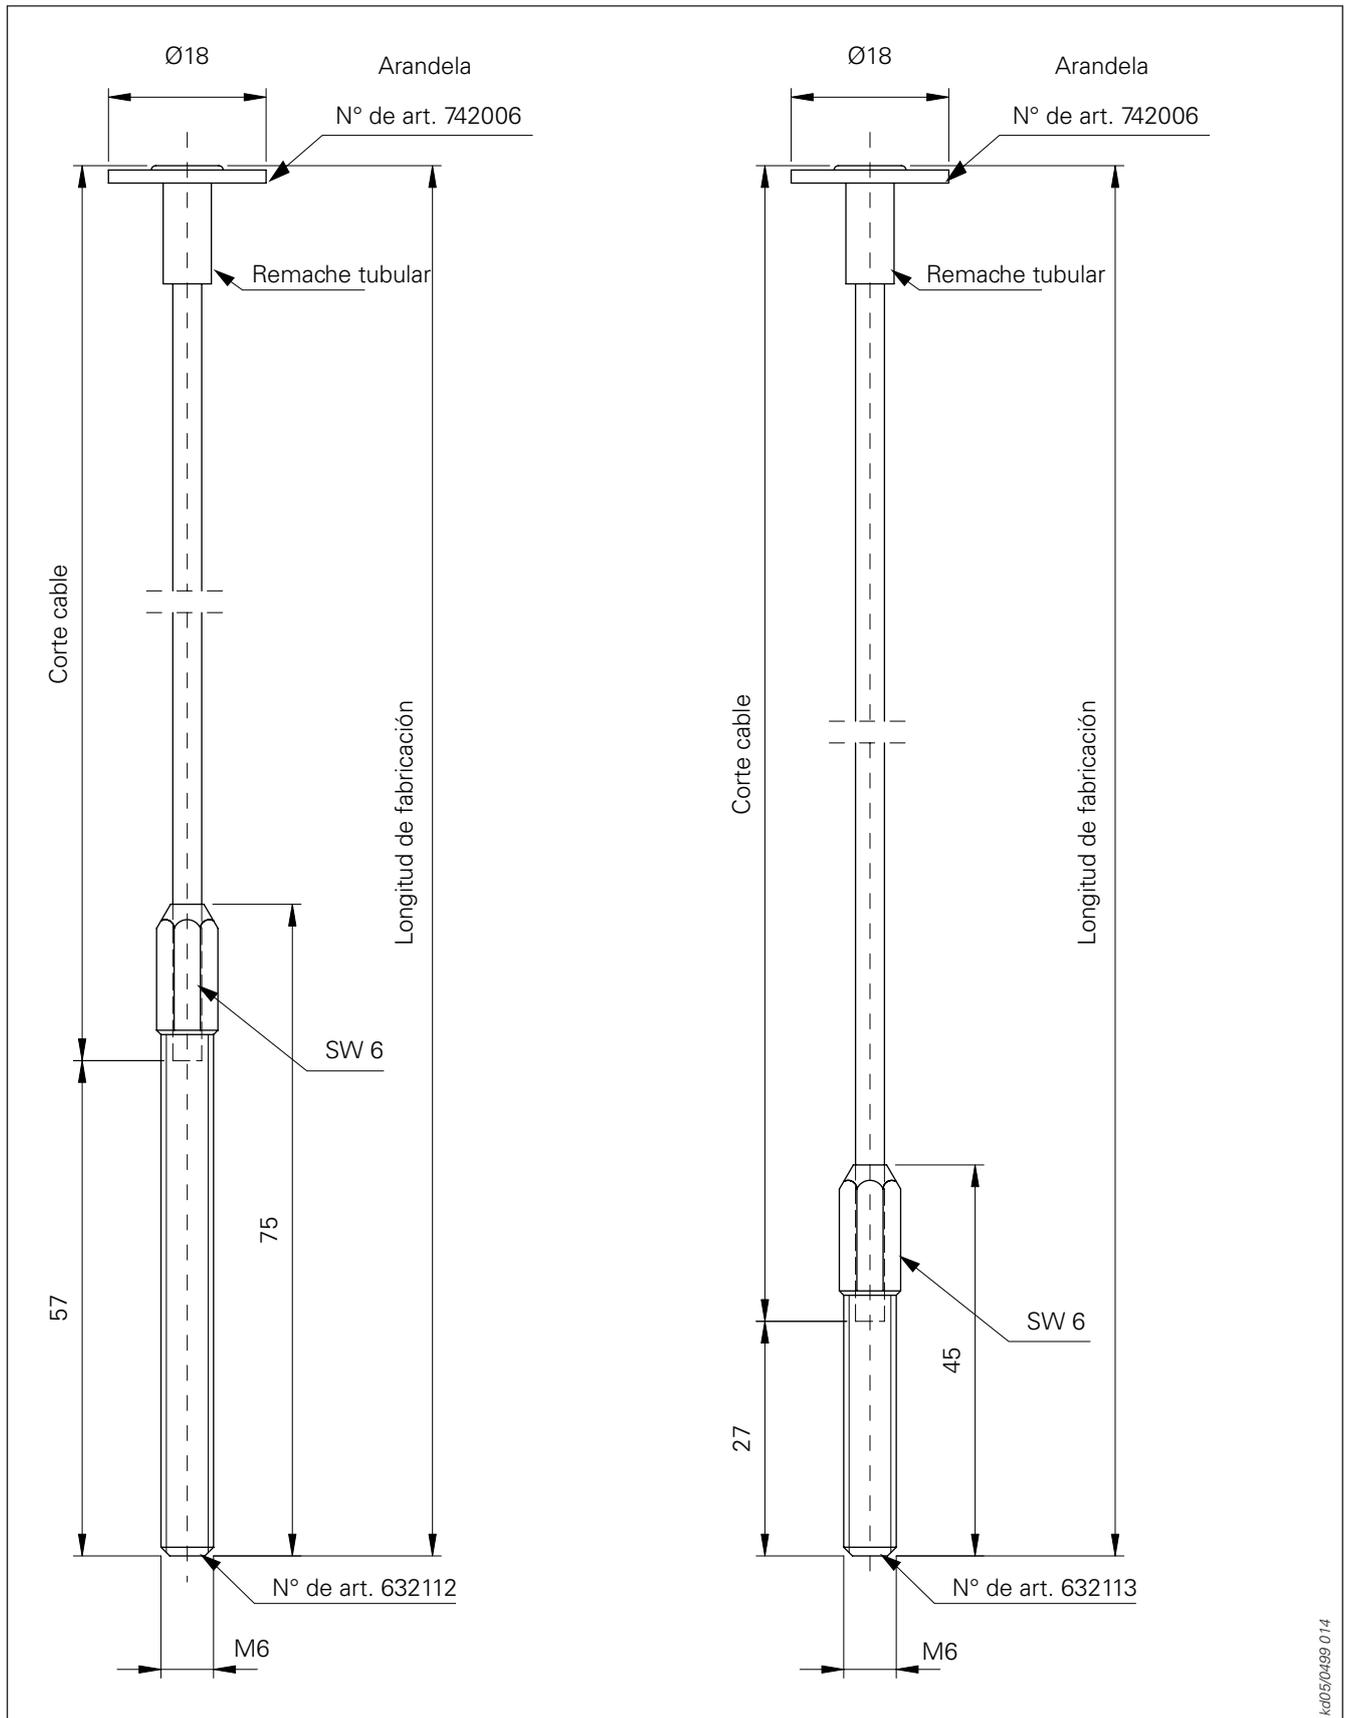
Cable tensor y pieza final roscada con principio de pinza en el soporte de cable tensor
